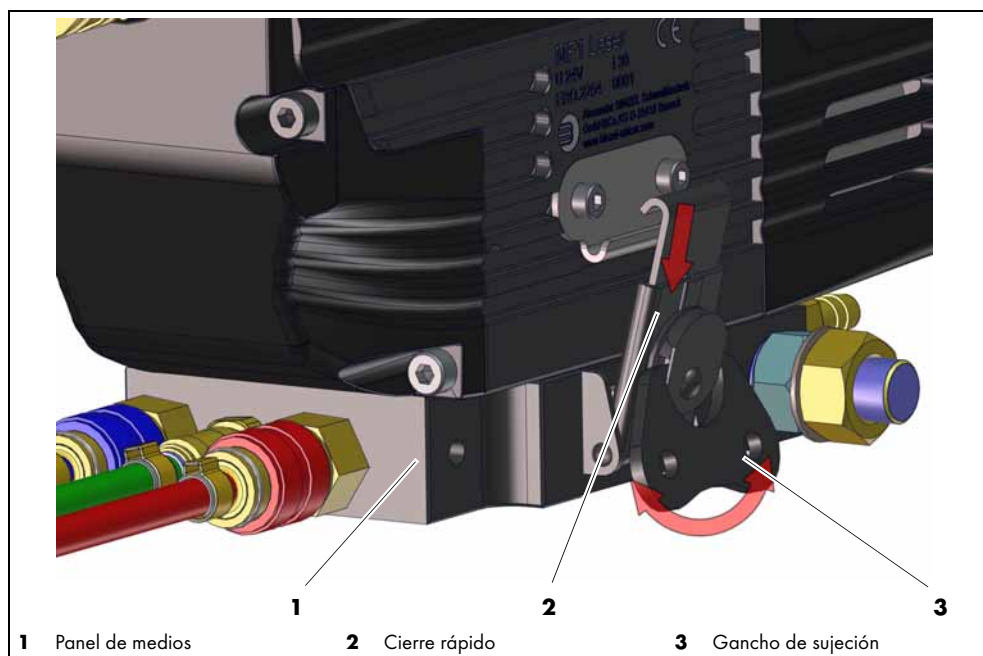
Montaje del alimentador MF1-Laser con panel de medios
